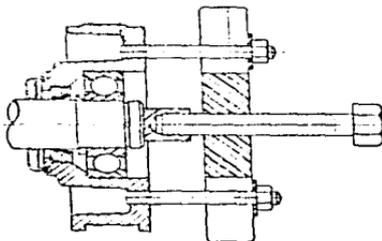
Extracción de baleros de bolas, encuadrando siempre la barra del extractor con el final de la flecha.
